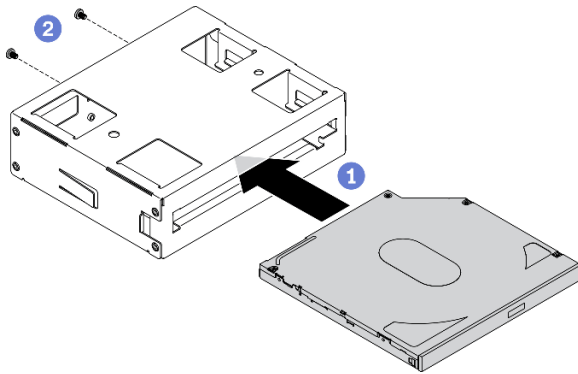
Installieren des flachen optischen Laufwerks im Laufwerkpositionsadapter
